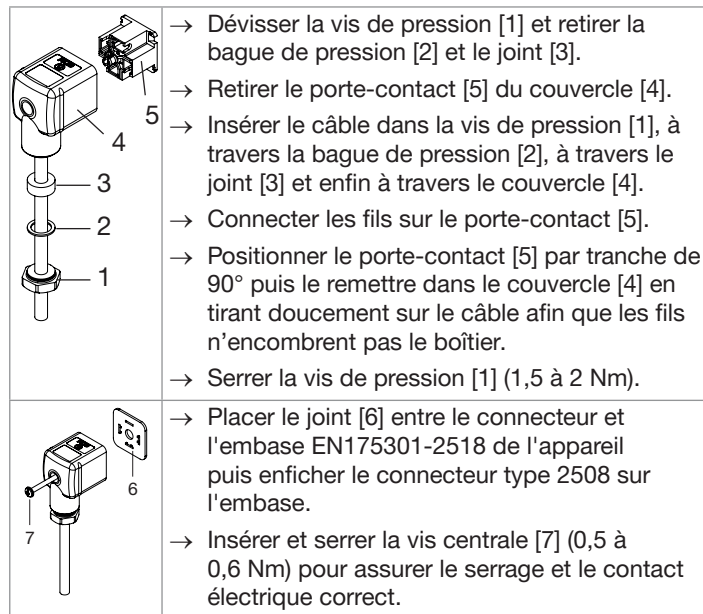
Assemblage de la prise femelle type 2518 (fournie)
